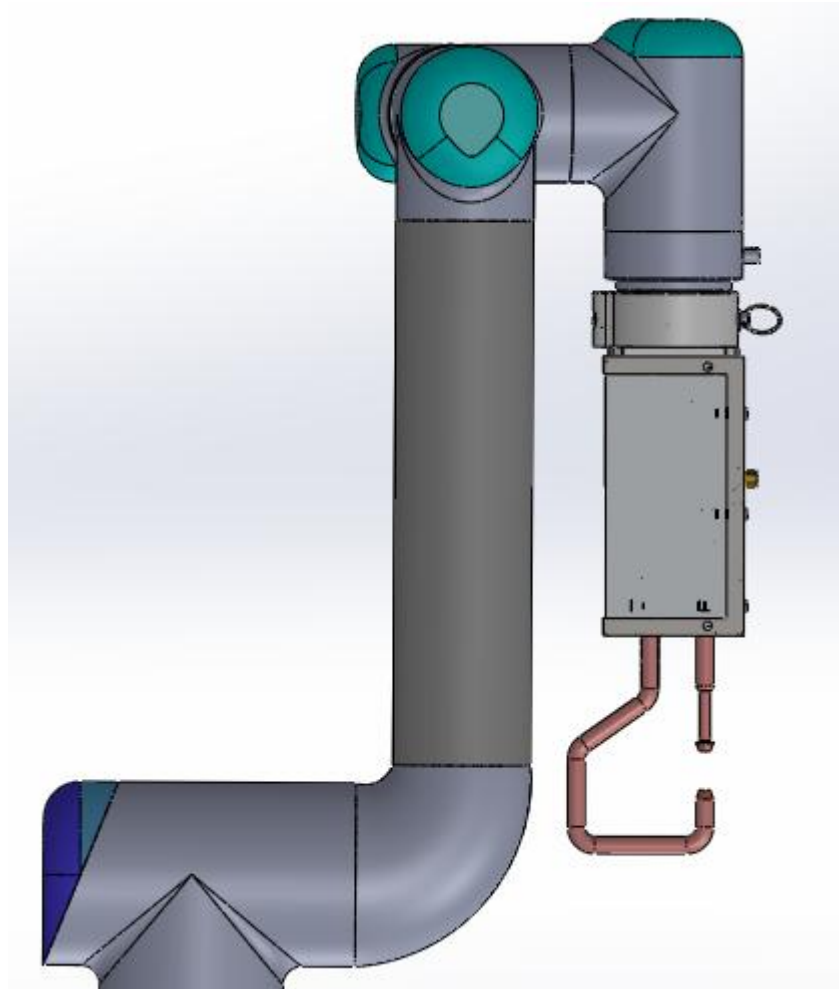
Vista lateral pinza de soldadura por puntos
